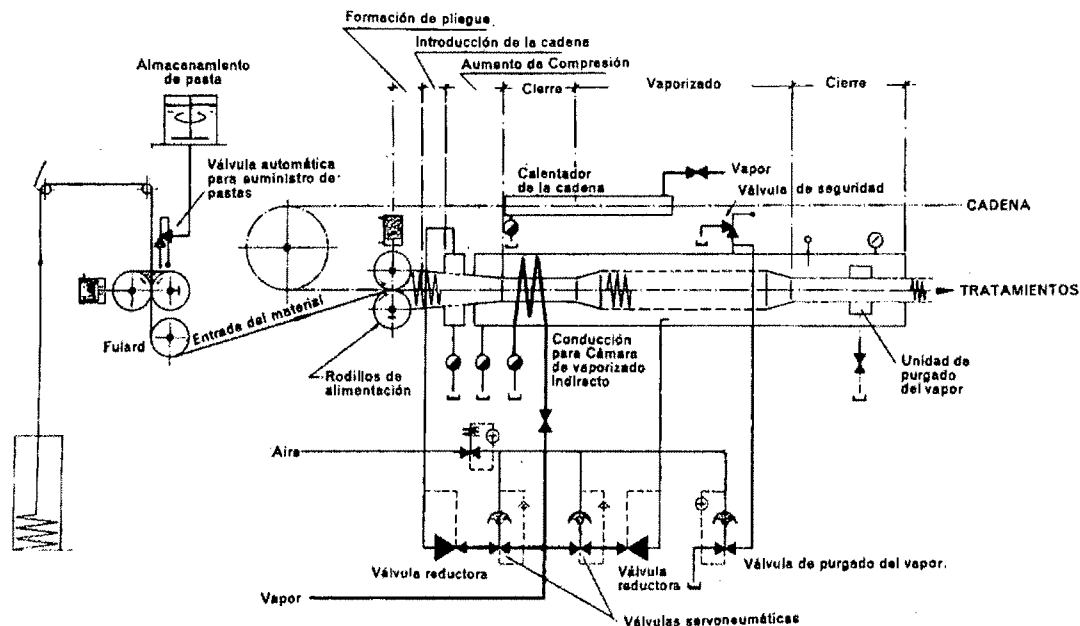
Esquema del túnel Segard-Serracant. Conjunto foulard-vaporizado.
